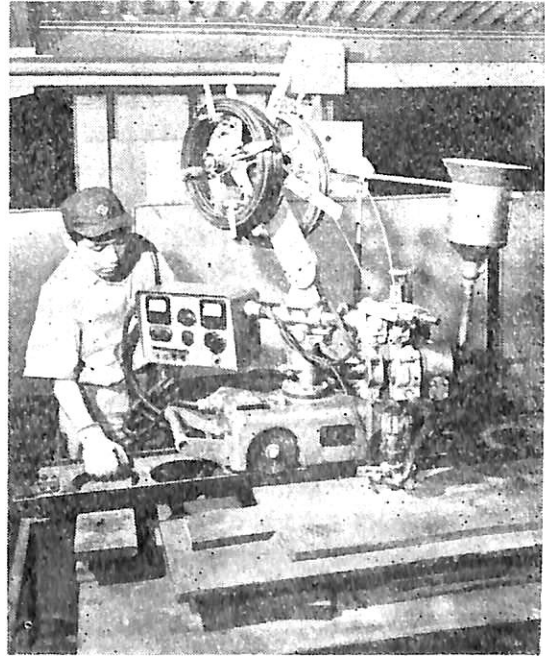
FN式a型サブマージ・アーク溶接装置の外観
